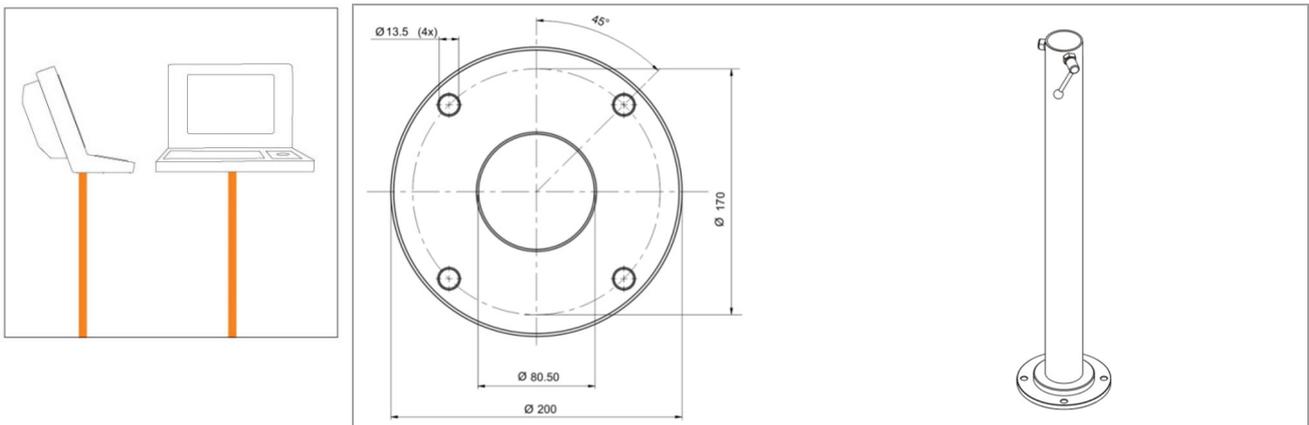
Bohrbild - Tragsystem für Bodenmontage
